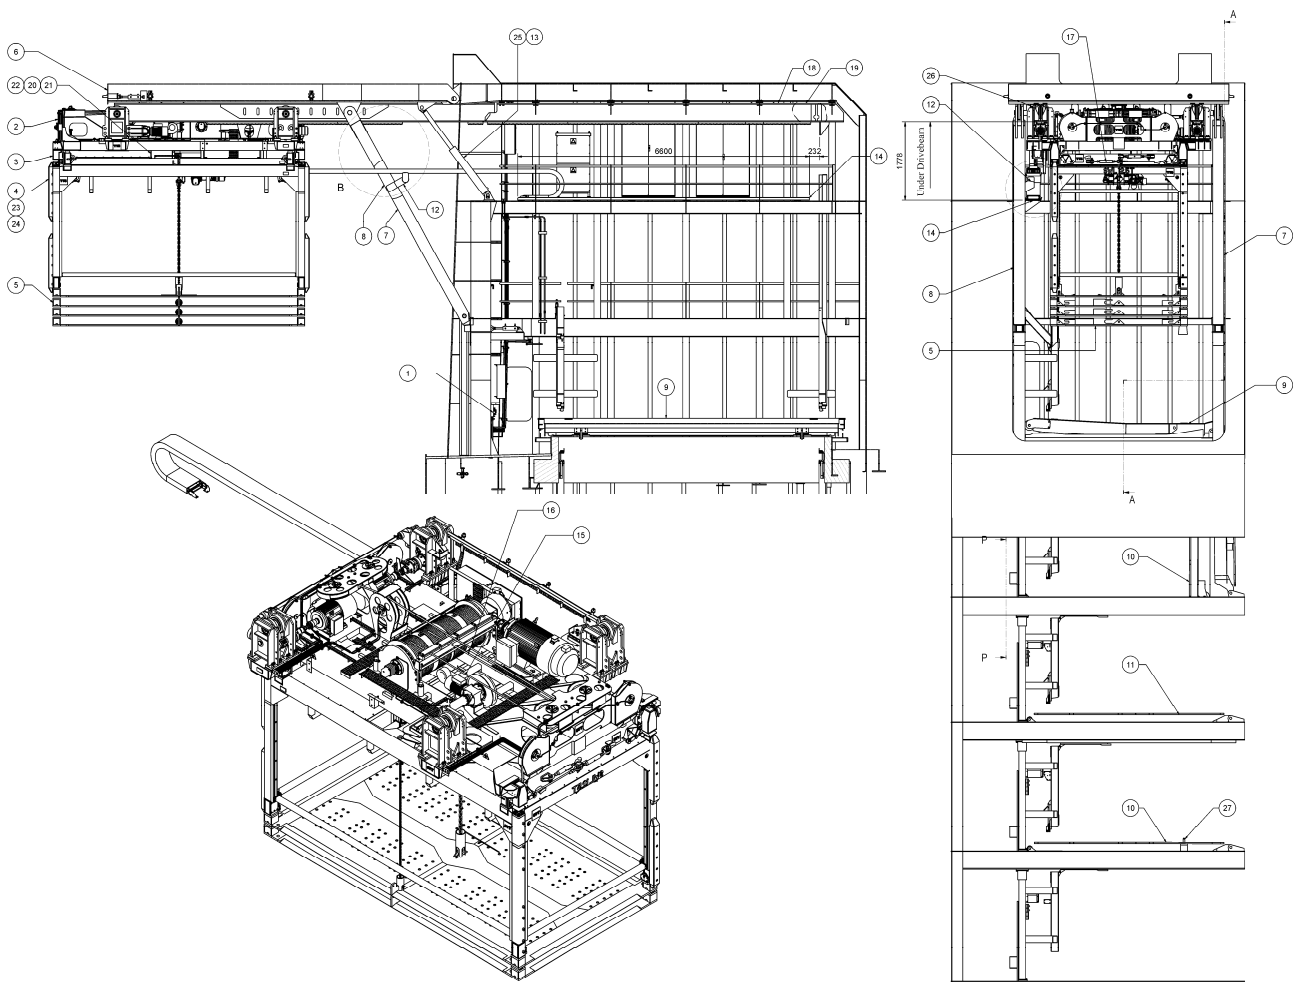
Вантажно-розвантажувальна система палет рефрижераторного судна: 1 – установка гідравлічна; 2 – металева змонтована конструкція візка; 3 – металева змонтована конструкція розподільника; 4 – клітка; 5 – додаткова нижня пластина; 6-8 – бокові двері; 9 – кришка люка верхньої палуби; 10 – кришка люка другої/четвертої палуби; 11 – кришка люка третьої палуби; 12 – кабель мережі підтримки лівосторонньої збірки; 13 – кронштейн циліндра на палубі; 14 – лоток для кабельного ланцюга; 15, 16 – трос; 17 – фаркоп; 18, 19 – лівий та правий приводи візків, відповідно; 20 – живлячий кабель; 21 – кронштейн кріплення кабелю; 22 – кабельні хомути; 23 – надпотужний роз'єм; 24 – кабельний ввід; 25 – гідравлічний циліндр; 26 – упор для датчика; 27 – вісь; 28 – пластина блокування внутрішньої позиції візка; 29-31 – шайба кріплення приводу Drivebeam; 32 – шайба; 33 – шестигранна самоконтр. гайка; 34 – гвинт головки блоку циліндрів
